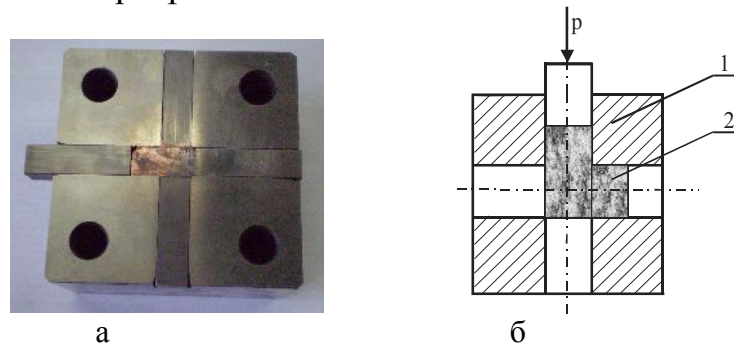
Установка для РКУ-прессования: фото матрицы – а; эскиз штампа – б: 1 – матрица; 2 – образец
